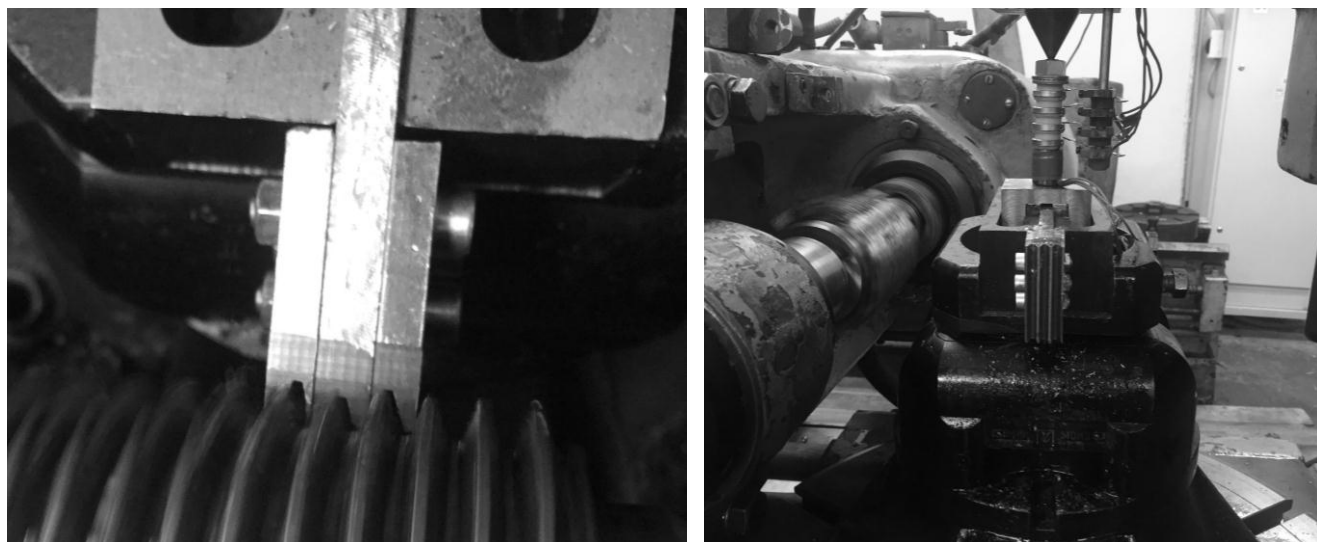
Обработка заготовки, имитирующей целое колесо
